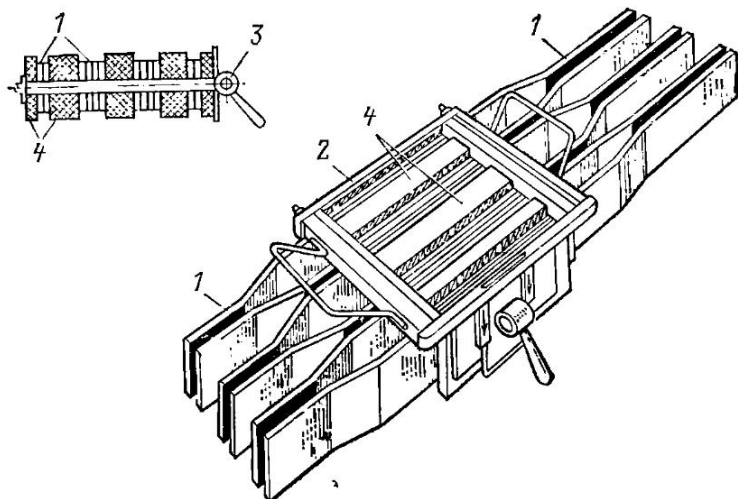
Кондуктор для сварки шин магистральных шинопроводов.
